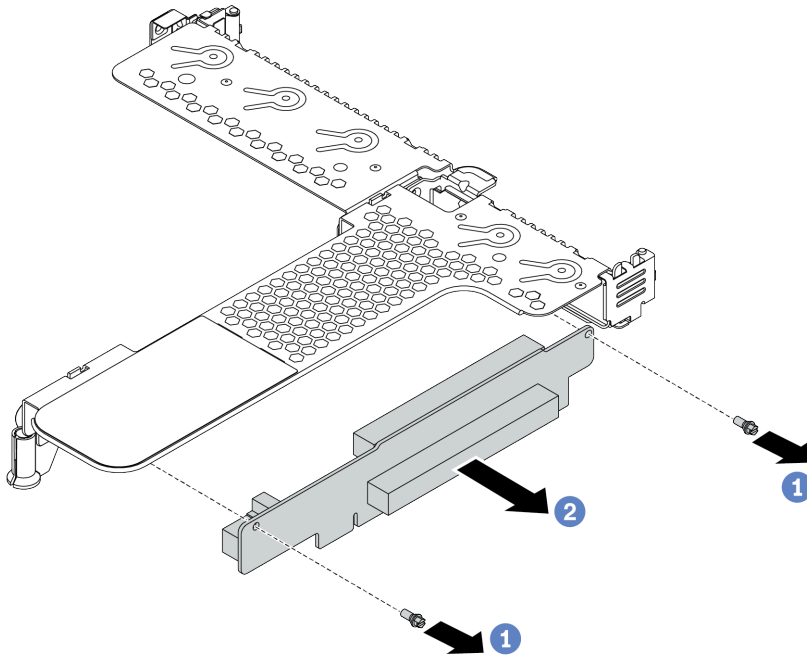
Entfernen der Adapterkartenbaugruppe
